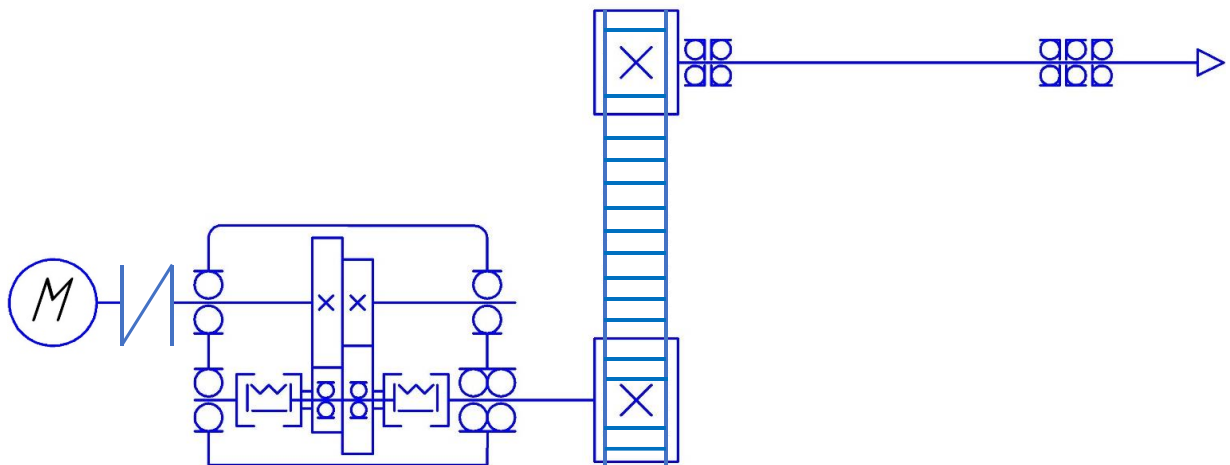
Привод головного руху токарно-револьверного багатоопераційного автомата з ЧПК мод. 11Б40ПФ4 до модернізації
